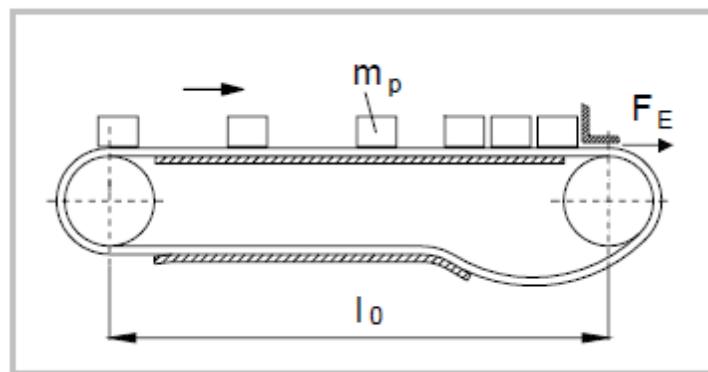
Componentes de una cinta Transportadora. Fuente: HabaCHAIN®, Slat and Conveyor Chains, Engineering Guide.
